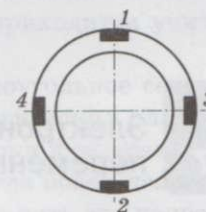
Схемы сварки кольцевых стыков:
